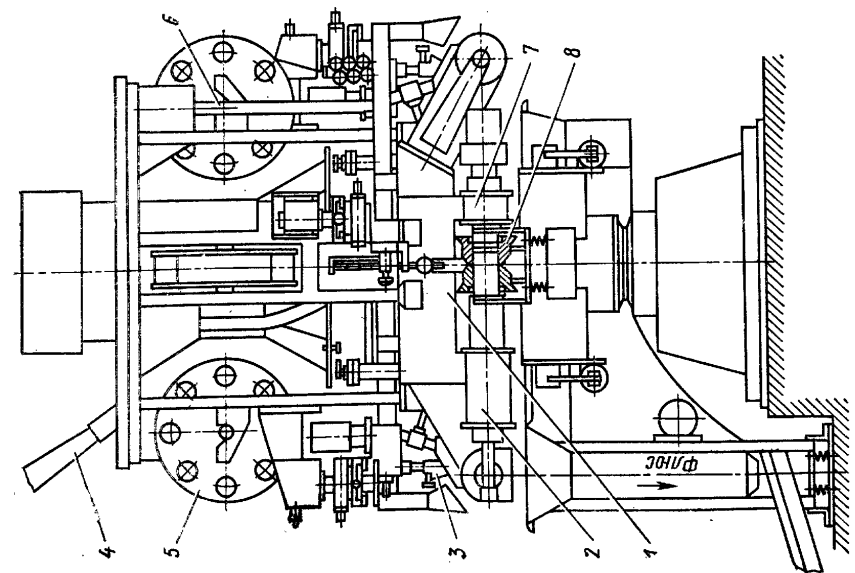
Автомат роторного типа для сварки опорного катка трактора
